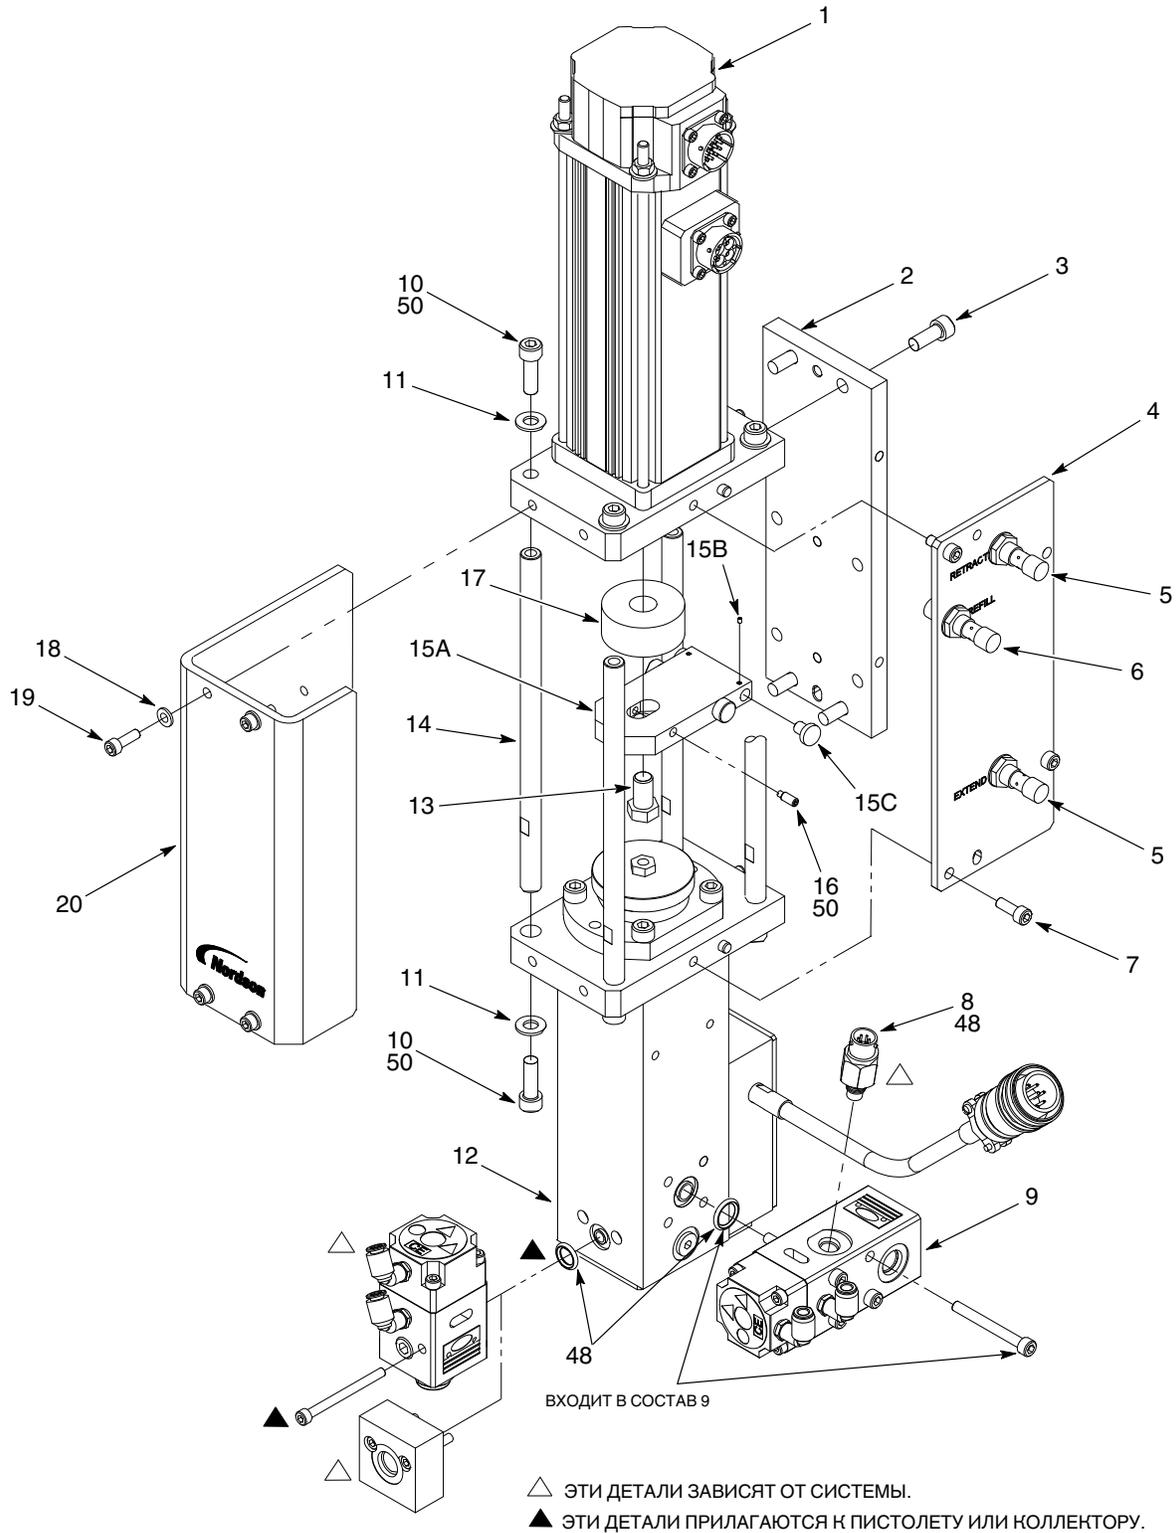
Запчасти для дозаторов S35 со 120/240-вольтовым нагревателем
